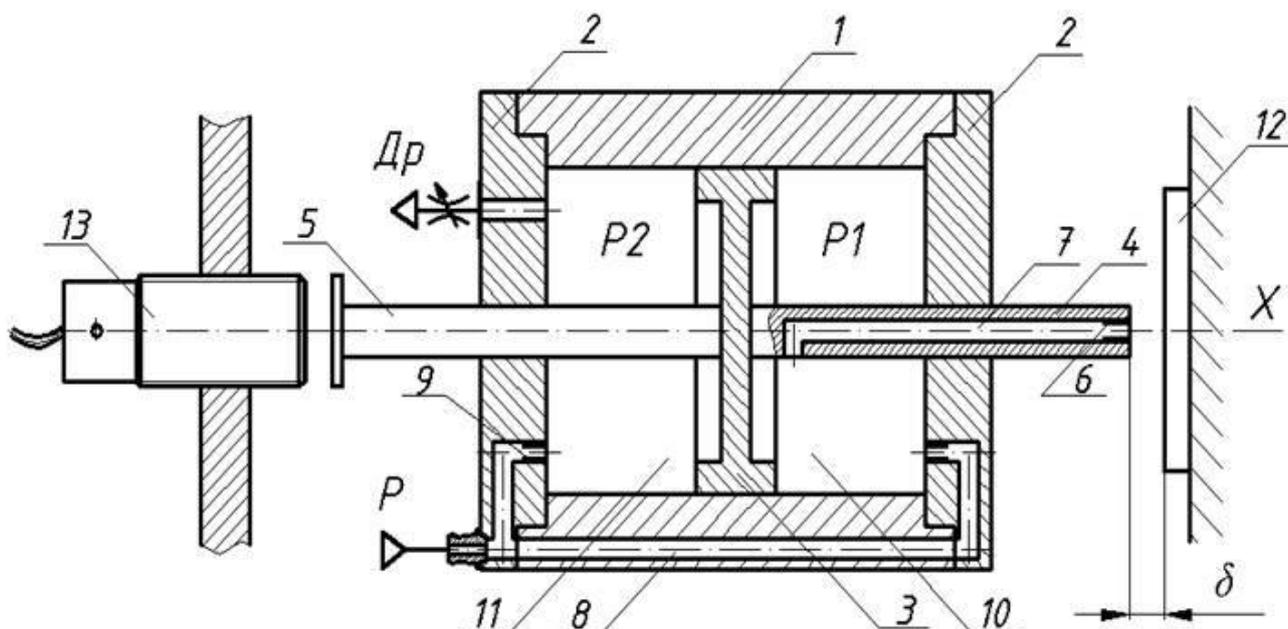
Поршневой широкопредельный следящий струйный датчик: 1 — корпус; 2 — крышки; 3 — поршень; 4, 5 — выходные штоки; 6 — измерительное сопло; 7, 8 — каналы; 9 — калиброванные ниппели; 10 — измерительная камера; 11 — камера противодействия; 12 — измеряемая поверхность; 13 — датчик положения аналоговый
